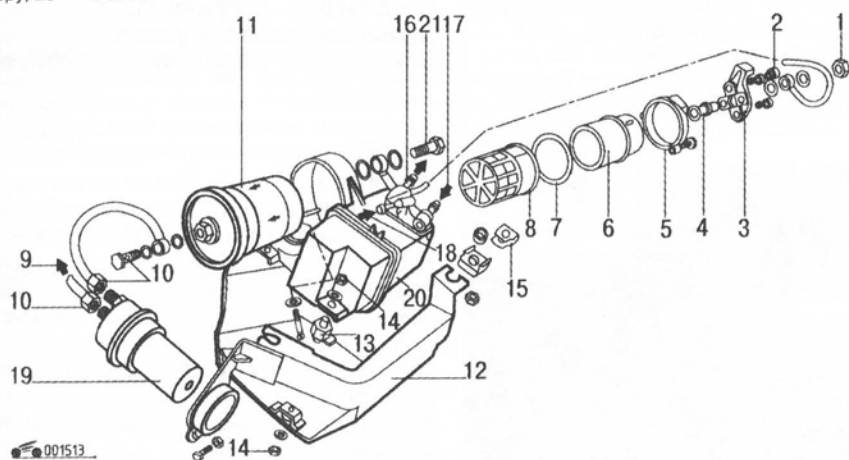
Топливный насос автомобилей с двигателем DOHC: 1, 14 – гайки; 2 – пробка; 3 – переходник; 4 – клапан; 5 – кольцо крепления; 6 – топливный насос; 7 – уплотнение; 8 – фильтр; 9 – топливопровод к распределителю; 10 – соединительная муфта; 11 – топливный фильтр; 12 – кронштейн; 13 – резиновый демпфер; 15 – пружинная скоба; 16 – штуцер обратной магистрали; 17 – штуцер трубопровода от подающего насоса; 18 – штуцер трубопровода возврата топлива; 19 – гидроаккумулятор системы топливоподдачи; 20 – бачок насоса; 21 – болт
